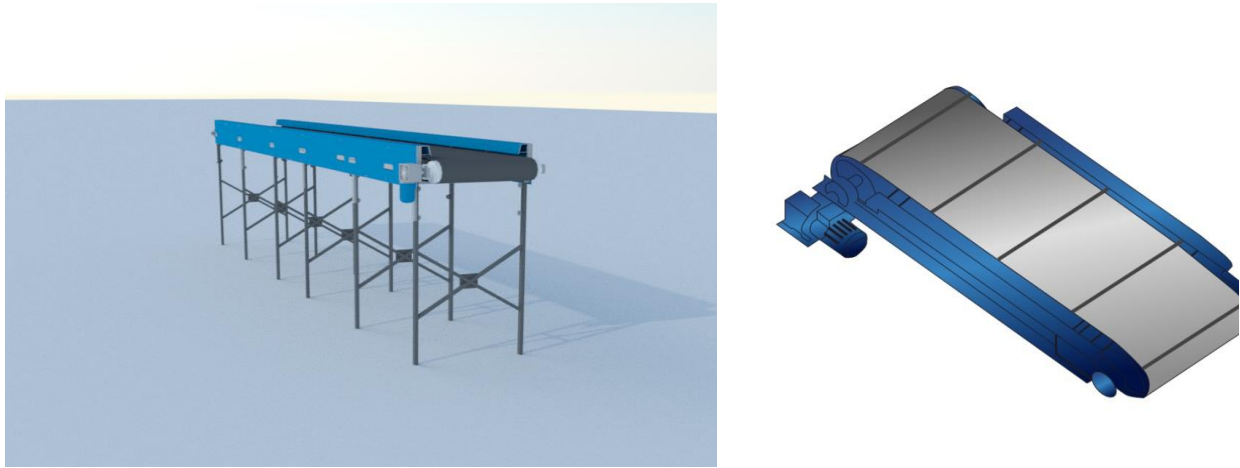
Ленточный конвейер основной сортировки и магнитный сепаратор
